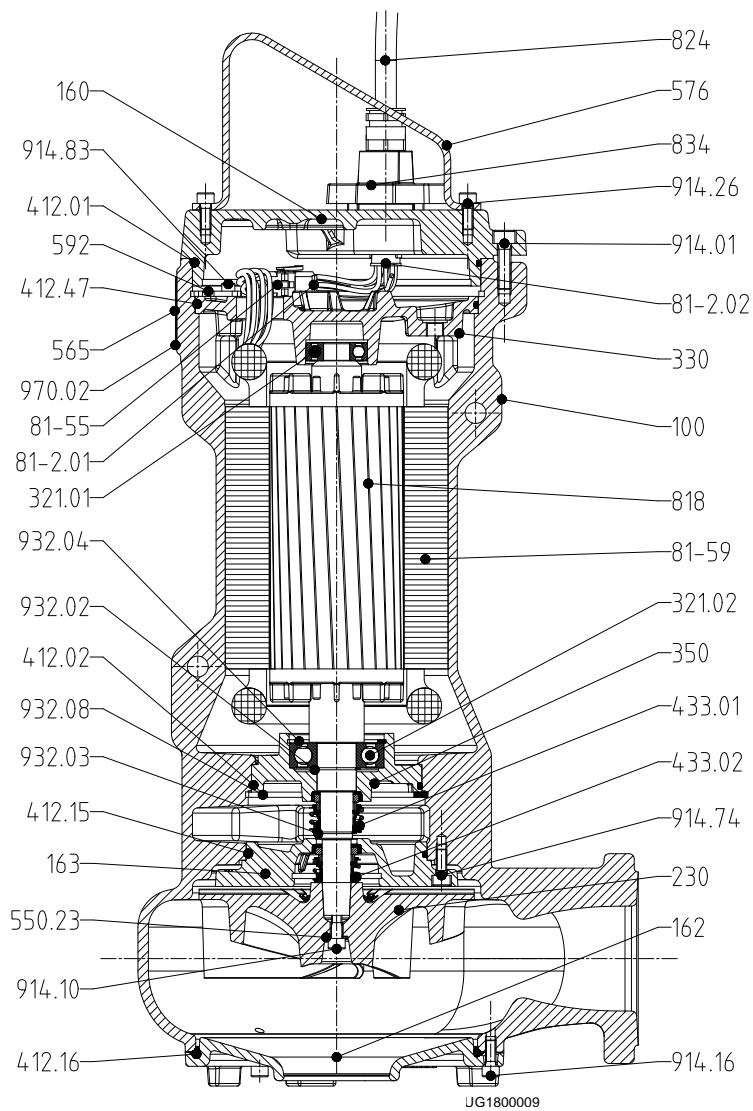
Сборочный чертеж для исполнения YS, рабочее колесо F-max
